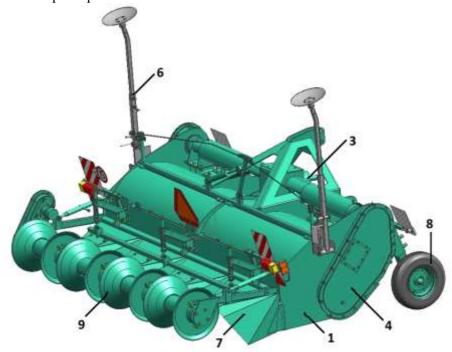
Общий вид агрегатов АПК с валкообразователем (дополнительное оборудование) 1 — рама; 3 — редуктор конический; 4 — бортовая передача; 6 — маркер; 7 — гребнеобразователь; 8 — колеса; 9 — валкообразователь.
